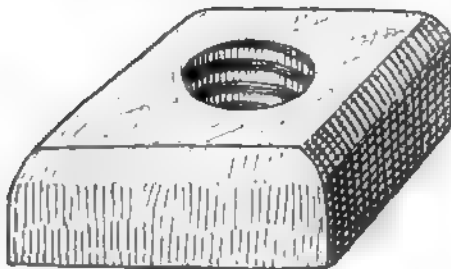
Schraubenmutter, um 180–260 n. Chr., nach einer Zeichnung des Prov.-Museums zu Bonn, Nat. GröÙe.
